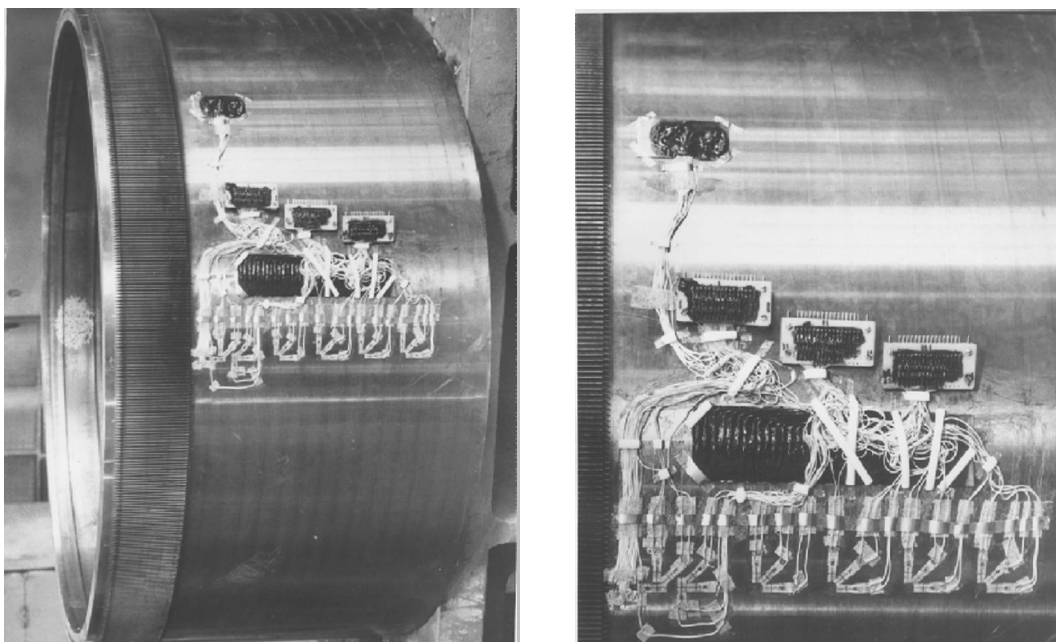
Гибкое колесо волнового редуктора механизма поворота передвижного миксера МП – 600 АС грузоподъемностью 600 т расплавленного металла
